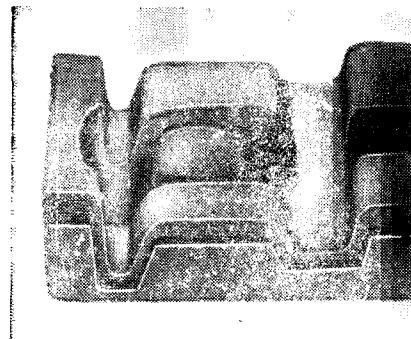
Сухая форма для термитной сварки рельсов.
